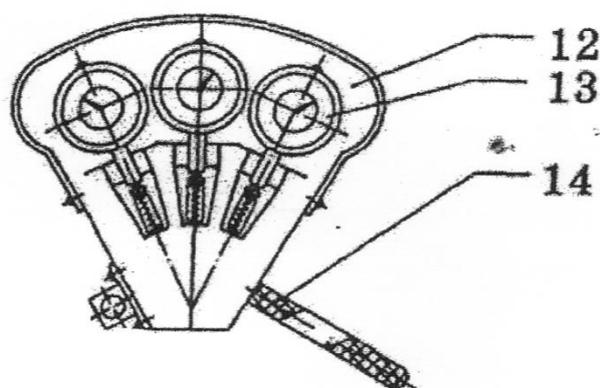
Приспособление для проверки несоосности гнёзд под вкладыши коренных подшипников:
